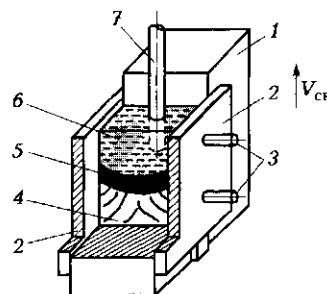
Схема процесса электрошлаковой сварки:
